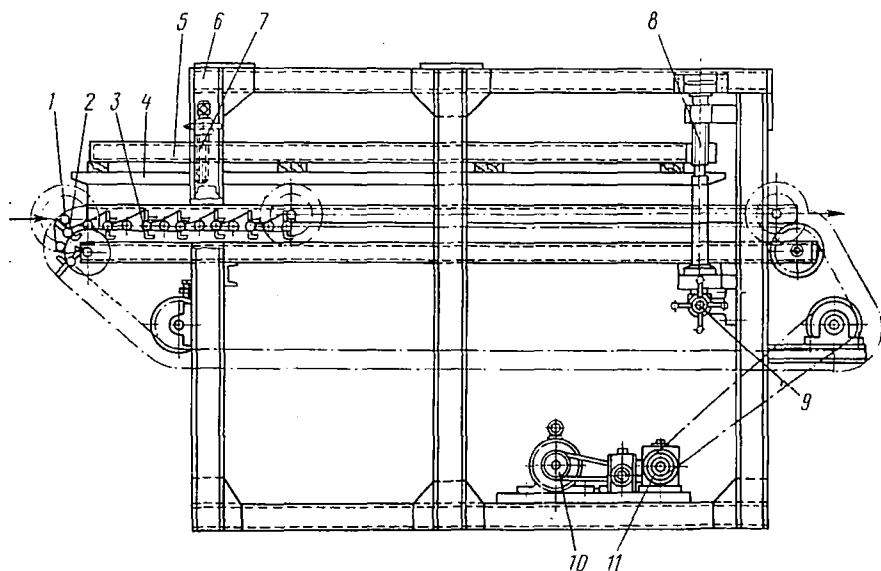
Станок для прокатки и калибровки минераловатных цилиндров
